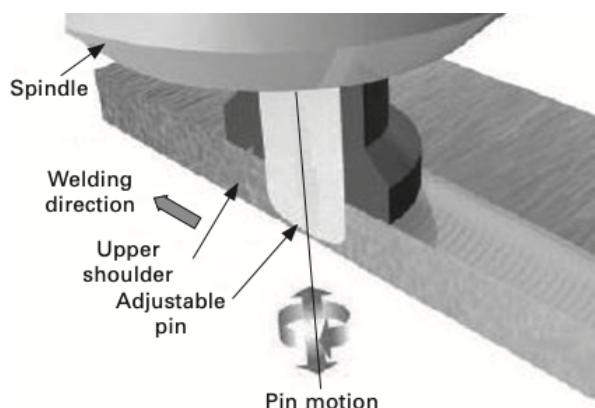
Sección de la herramienta FSW con pasador ajustable. [9]
